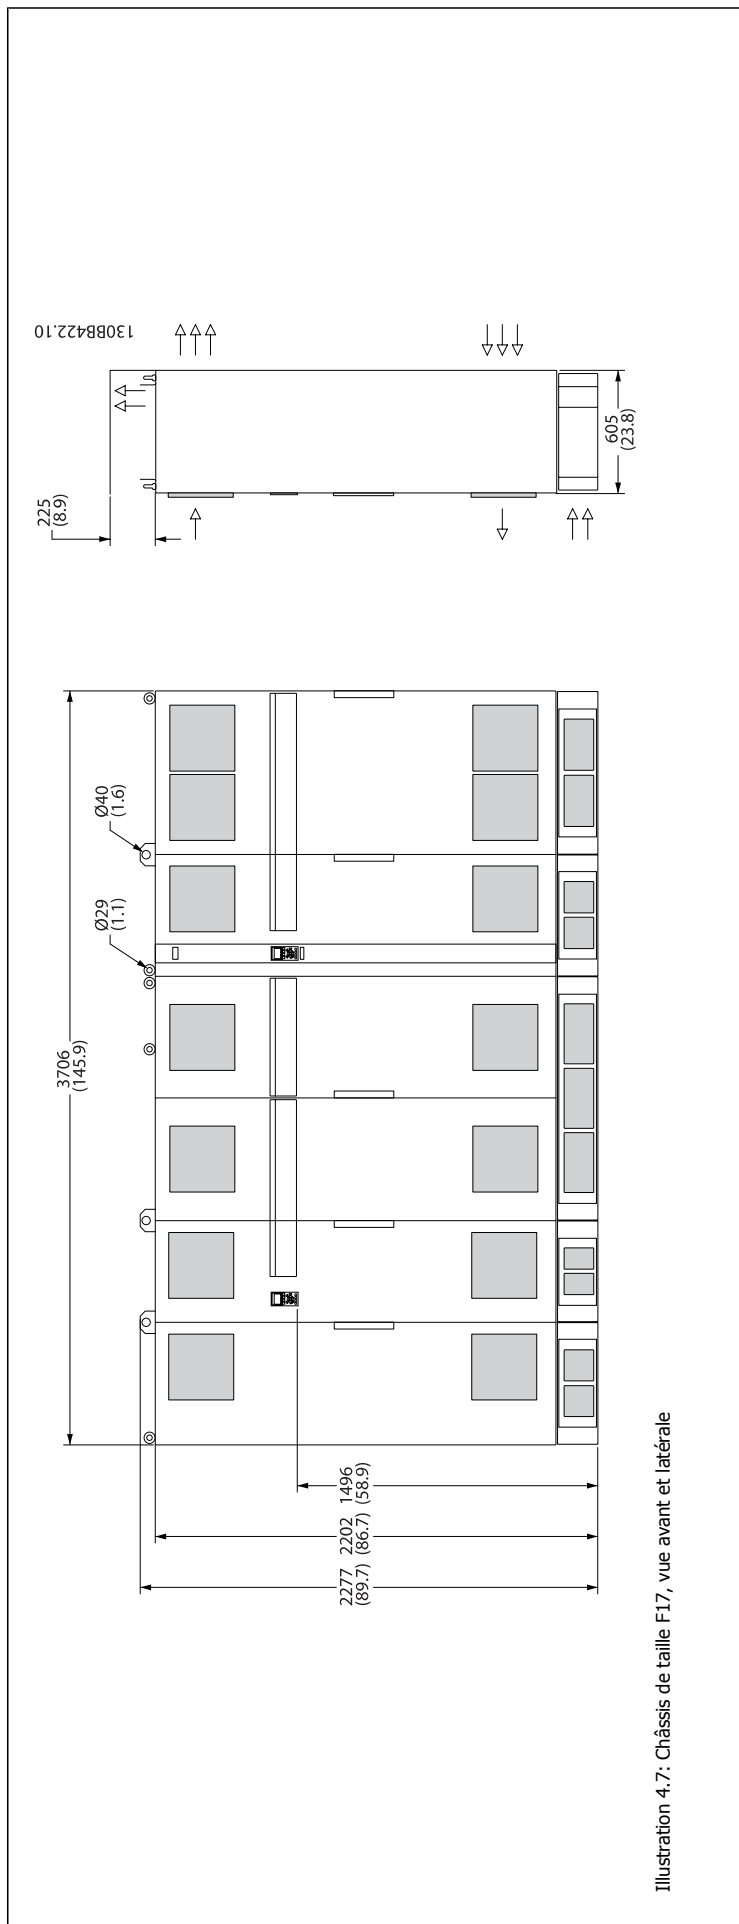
Châssis de taille F17, vue avant et latérale
